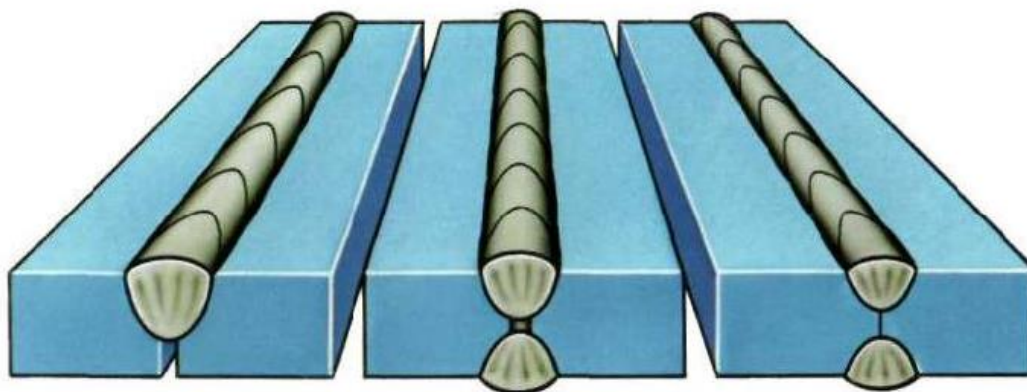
Типы дефекта (непровар) сварного шва.
